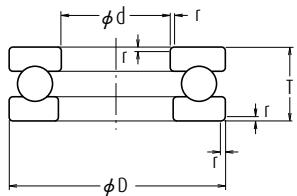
Rodamientos de Bolas de Empuje de Una Sola Dirección
